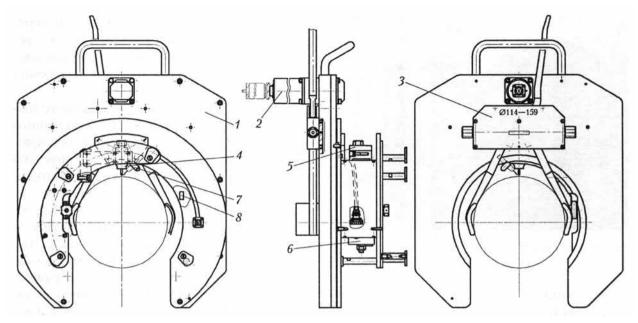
Конструктивная схема построения головок сварочных АДЦ 628.03.00.000, АДЦ 629.03.00.000, АДЦ 630.03.00.000: 1 – неподвижный корпус; механизмы: 2 – вращения (вращатель); 3 – зажима; 5 – АРНД; 6 – поперечного перемещения; 4 – горелка; 7 – узел канала подачи присадочной проволоки (узел лайнера); 8 – датчик пространственного положения неплавящегося электрода (инклинометр)
